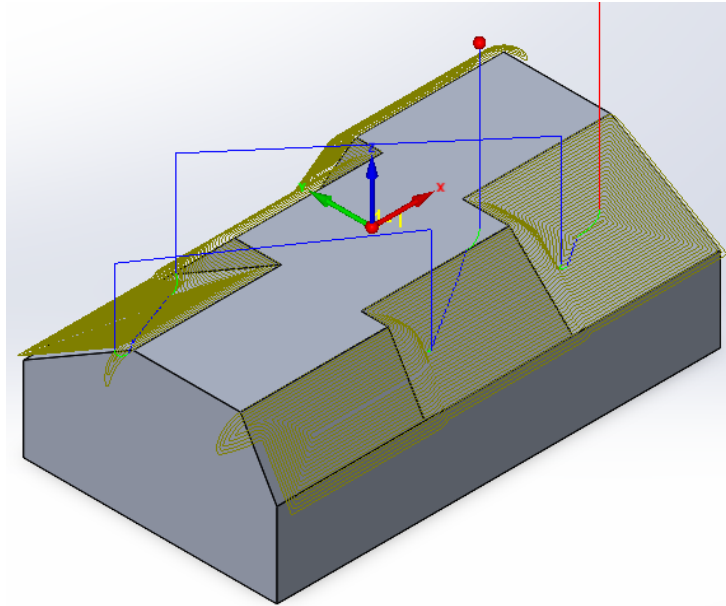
Trajetória executada durante a operação de maquinagem passagem constante 3D turbo
